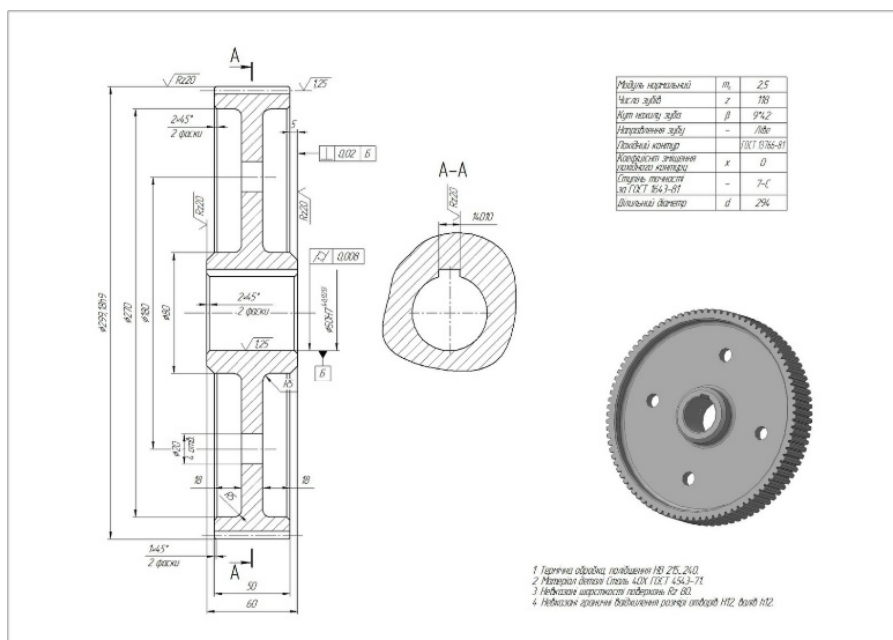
Креслення та 3D модель зубастого колеса редуктора
